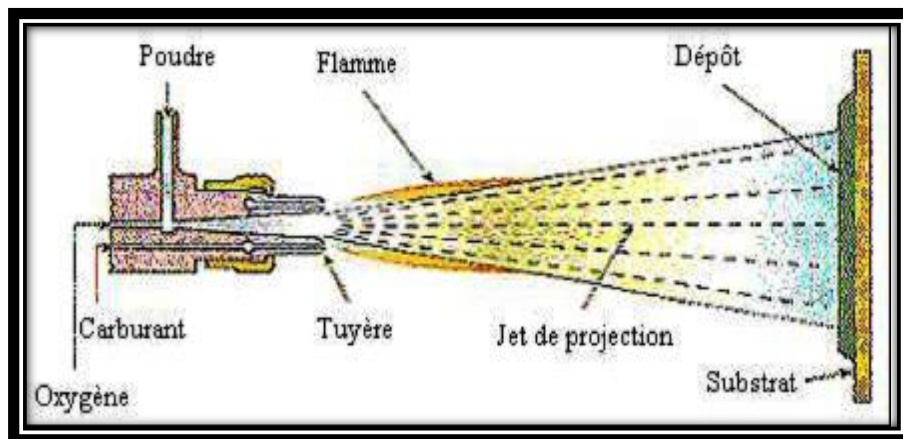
Schéma du principe d'un pistolet flamme-poudre [5].
